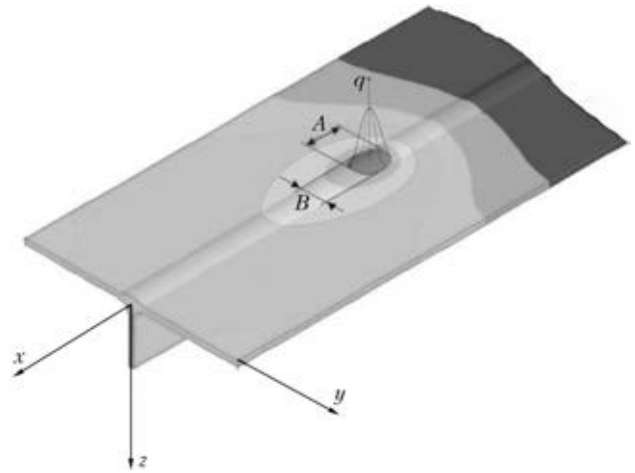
Схема сварочного источника нагрева при сварке образца панели прорезным швом (A — длина сварочной ванны; B — ширина сварочной ванны, q — гауссово распределение тепловой мощности)
